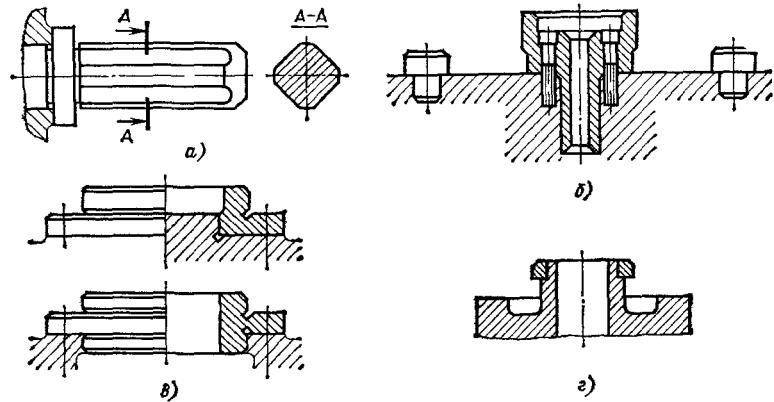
Пальцы для установки заготовки цилиндрическим отверстием:
